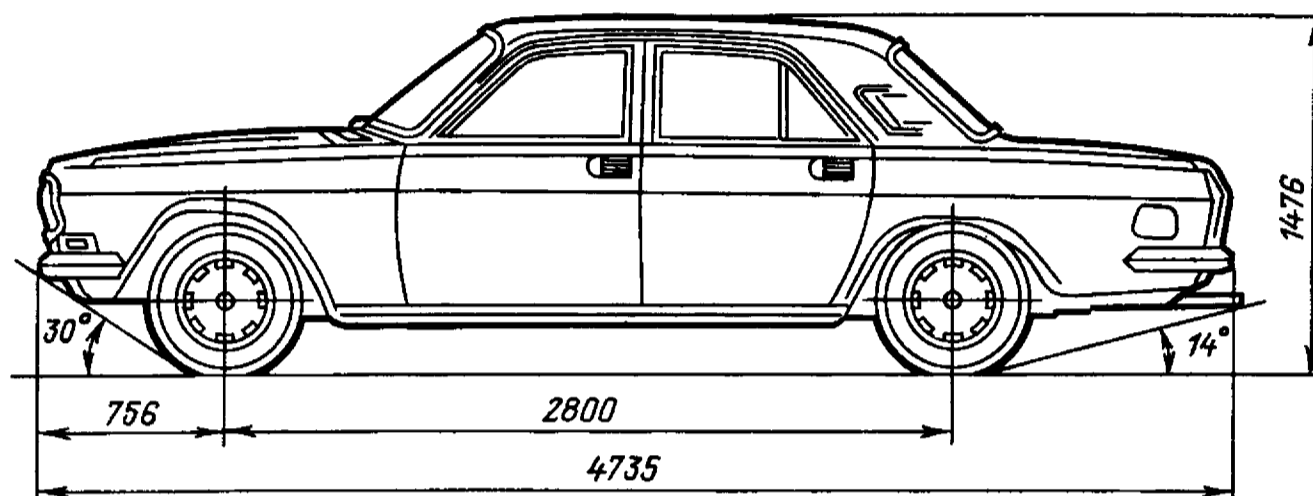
Автомобиль ГАЗ-24-10 «Волга» и его габаритные размеры
